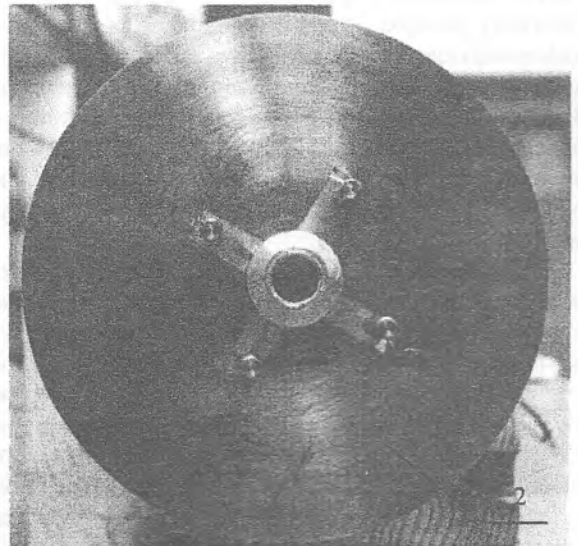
Общий вид макета для вращения заготовки распиловочного диска, с установленной консольной оправкой
